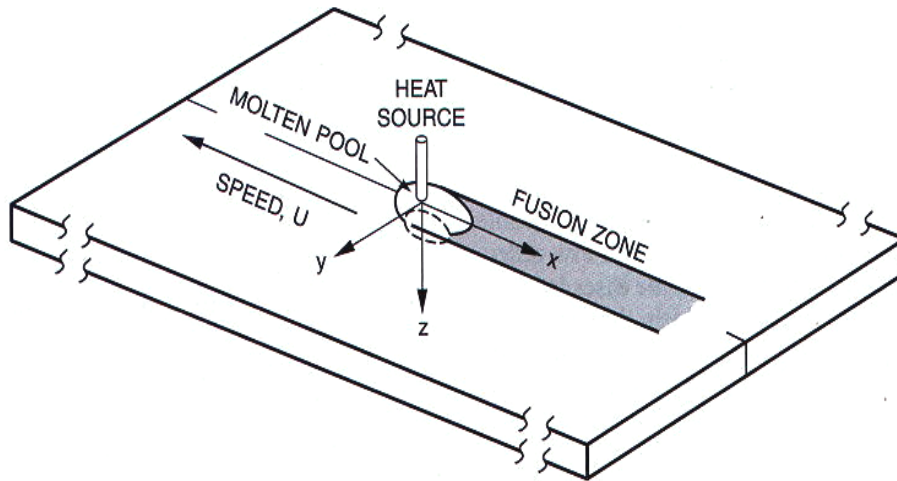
Sistema de coordenadas para el análisis de la transferencia de calor en soldadura (22).
